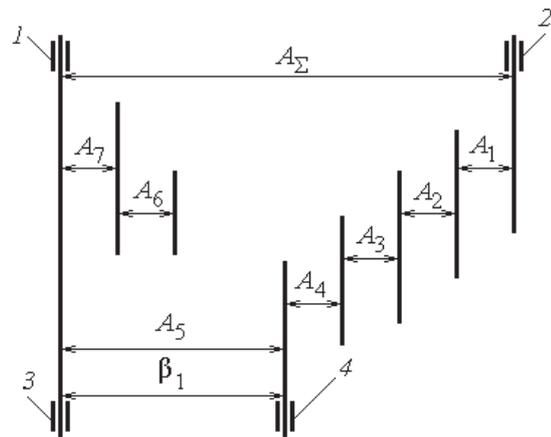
Схема размерной цепи коробки отбора мощности: 1, 2 – оси вращения зубчатых колес; 3, 4 – оси отверстий под подшипники в корпусе передачи
